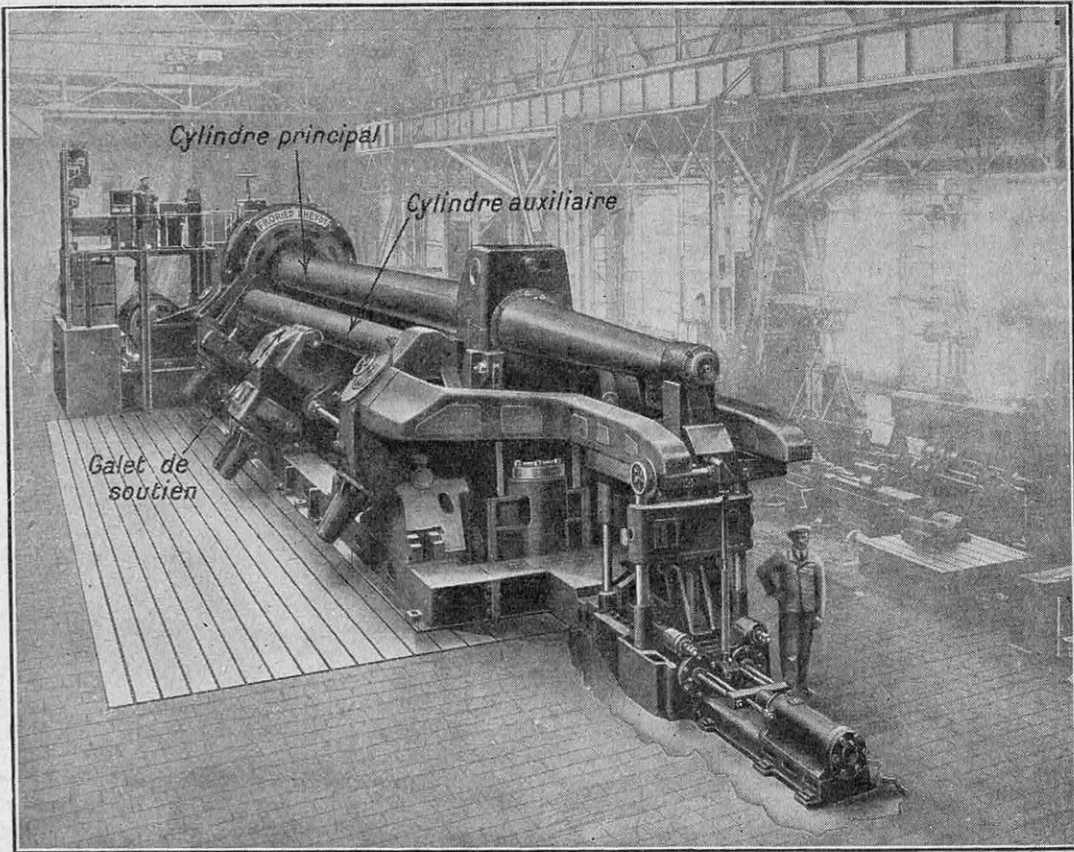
MACHINE A CINTRER COLOSSALE, AVEC COMPENSATEUR DE FLEXION
